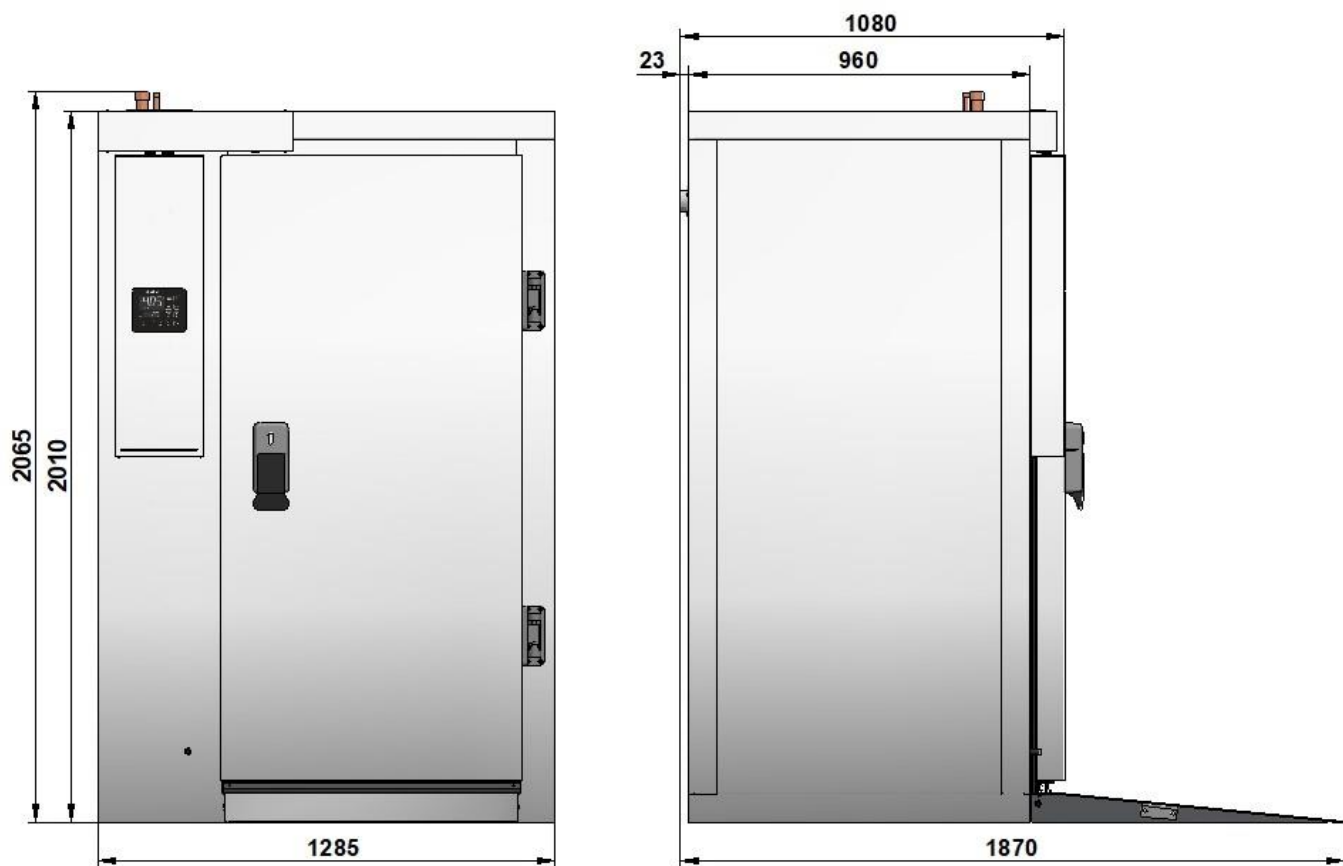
Габаритные размеры камеры ШОКК-20Т
